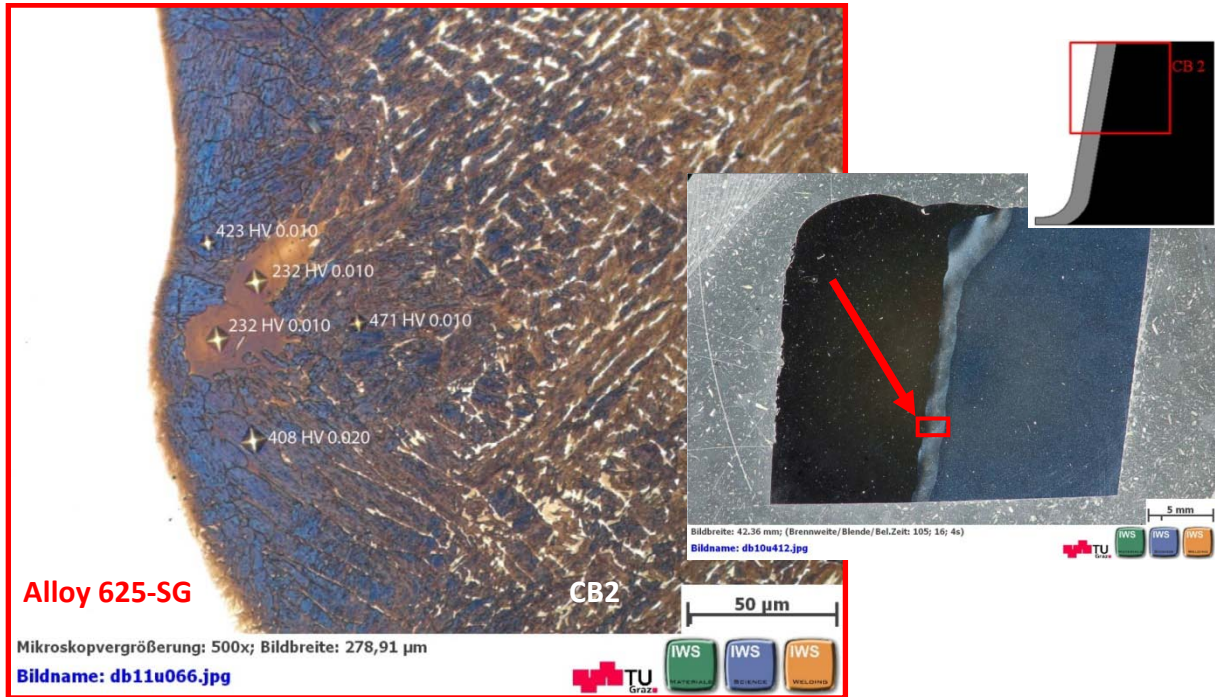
Mikrohärtmessungen der WEZ der Flanke des CB2 im “as-welded“-Zustand; Fülldrahtelektrode (4. Probe), Ätzung: mod. LB II.
